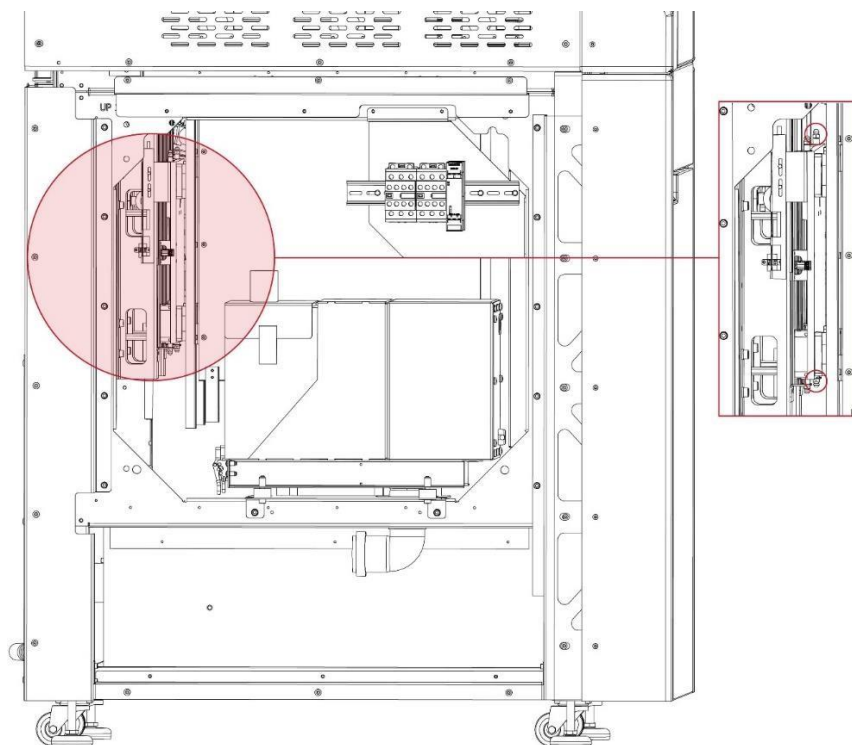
Месторасположение смазочных ниппелей - вид сбоку.
